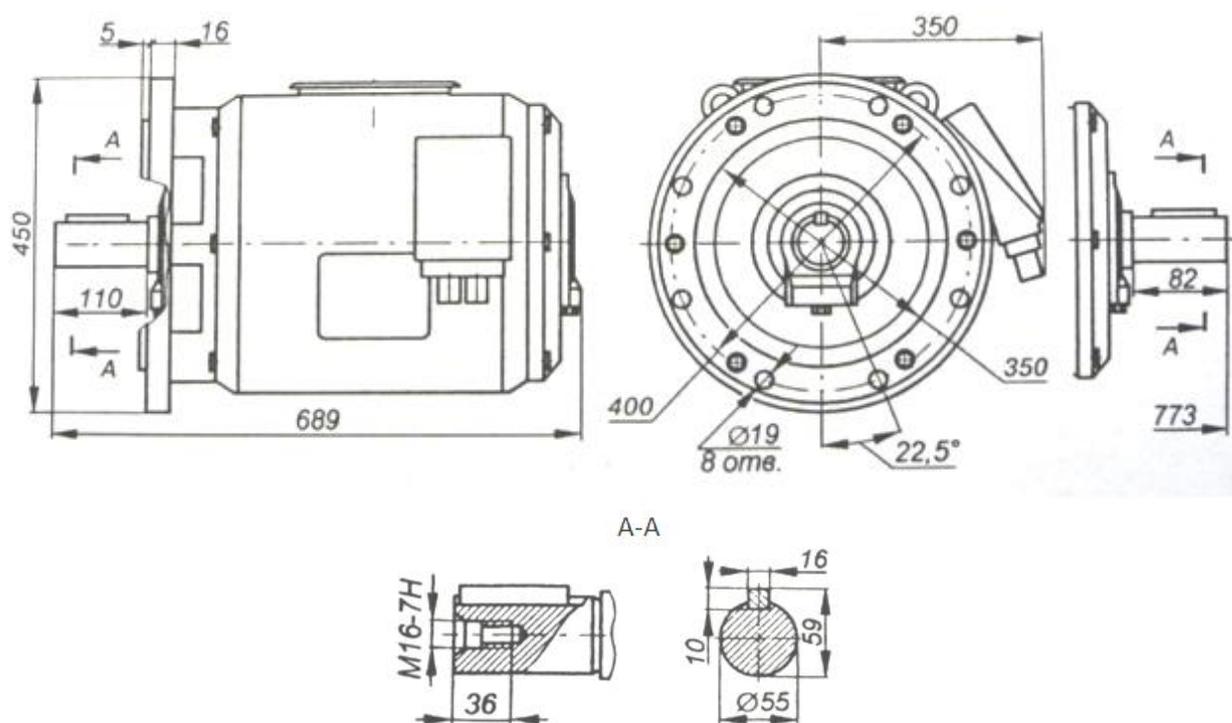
Общий вид, габаритные, установочные и присоединительные размеры
